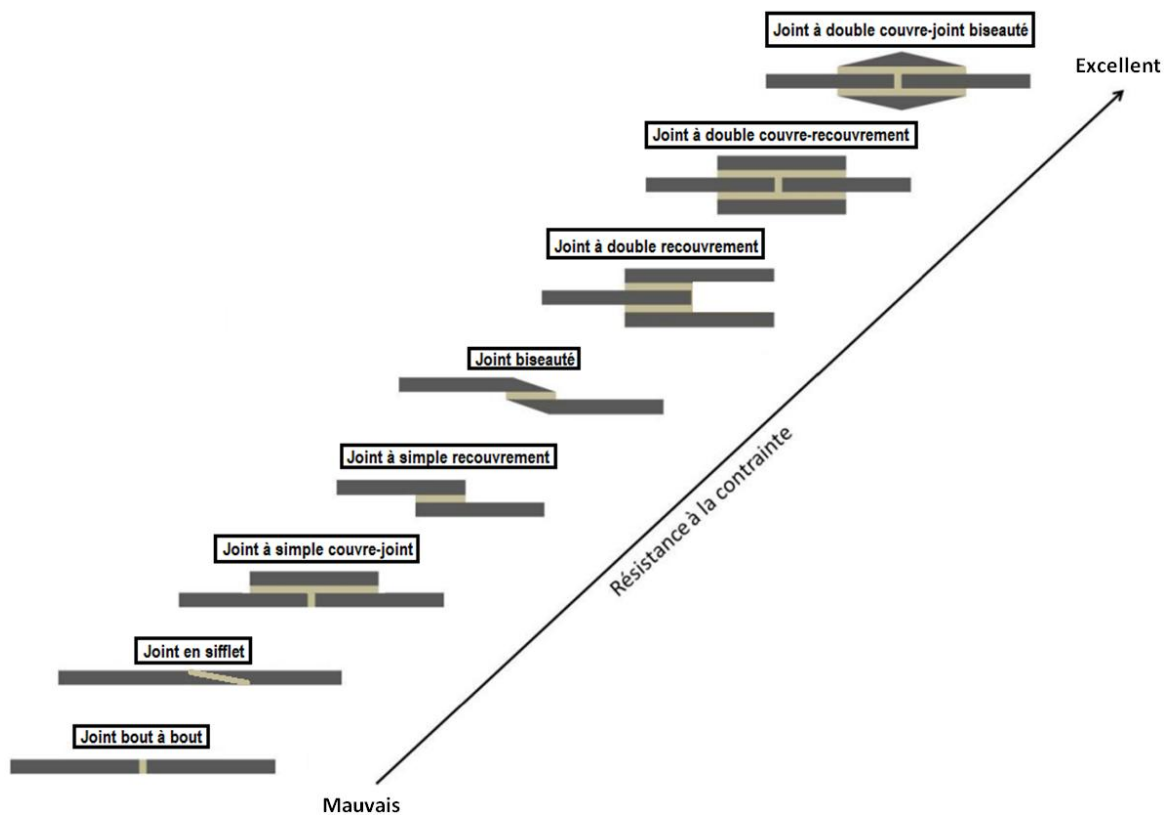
Principaux types d'assemblage de plaques par collage [58].
